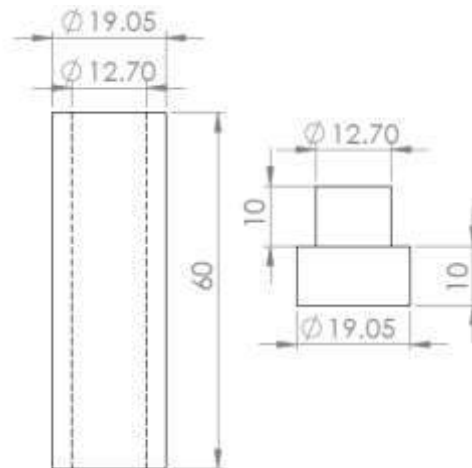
Diseño de crisol #2 para fundición (cotas en mm)
